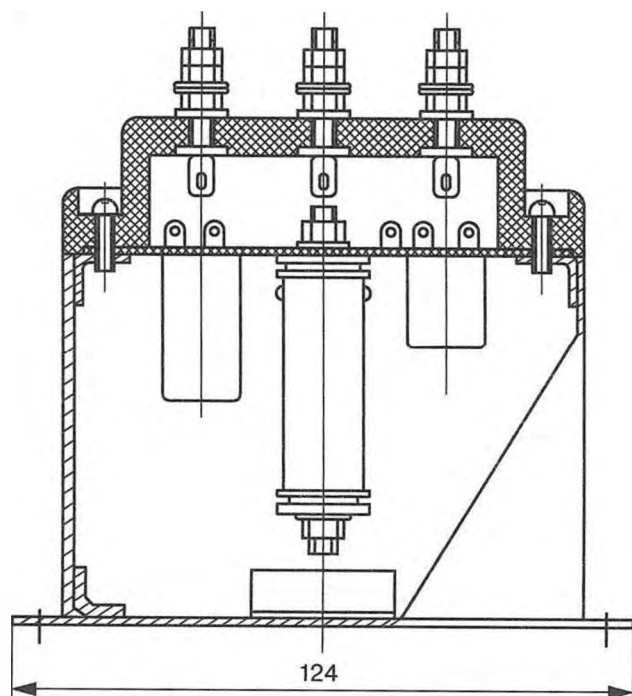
Габаритные и установочные размеры блока конденсаторного КБ-7 и КБ-8
